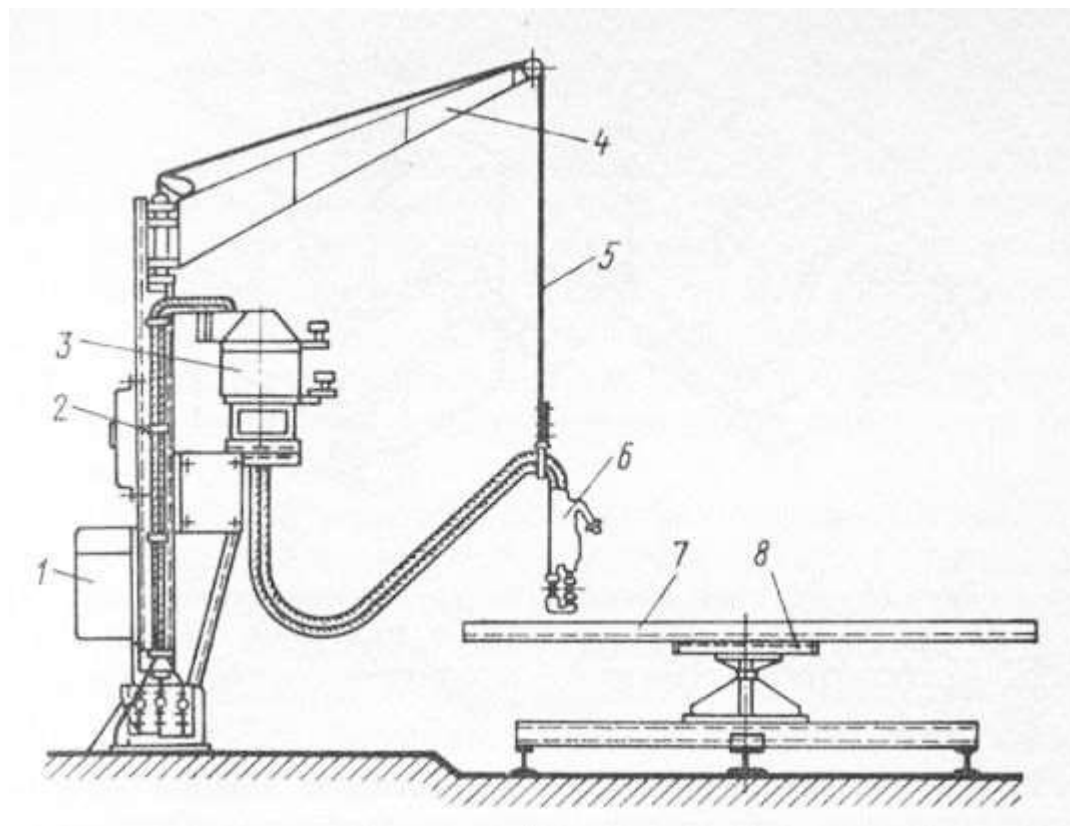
Установка СМЖ-54В для сварки арматурных каркасов: 1 – контргруз, 2 – стойка, 3 – сварочный трансформатор, 4 – консоль, 5 – канат, 6 – сварочные клещи, 7 – кондуктор, 8 – поворотный стол
